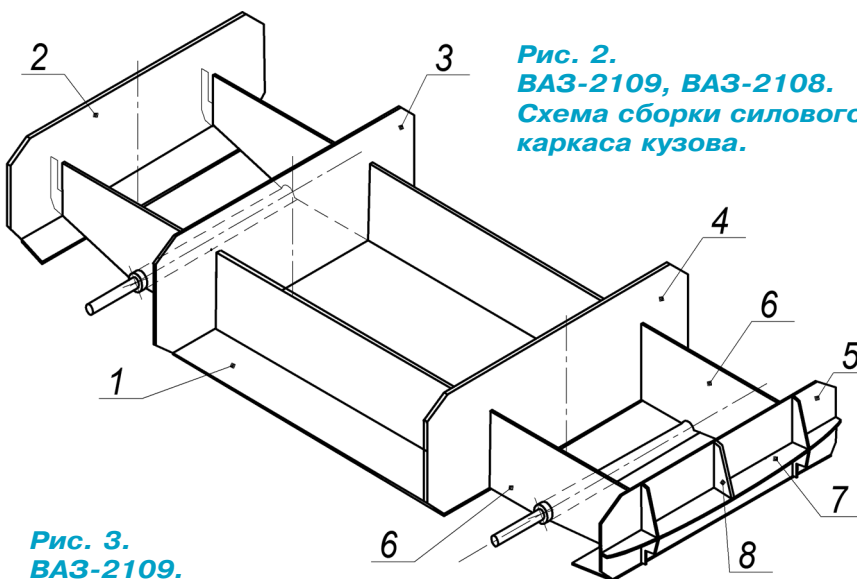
ВАЗ-2109, ВАЗ-2108. Схема сборки силового каркаса кузова.
